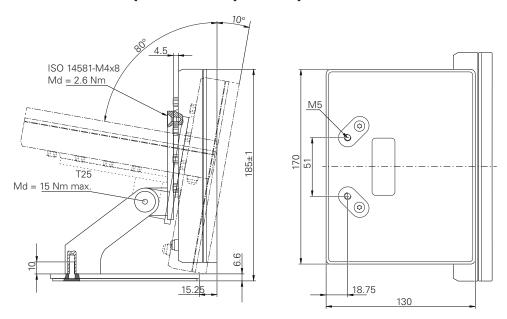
Dimensões do aparelho com pé de suporte Multi-Pos
